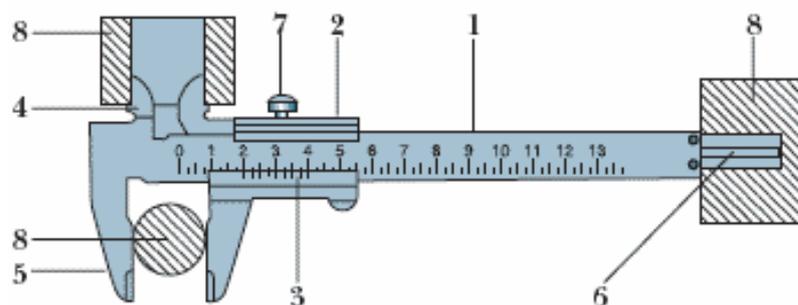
1 – штанга; 2 – ползун; 3 – нониус; 4 – верхние губки; 5 – нижние губки; 6 – глубиномер; 7 – стопорный винт; 8 – деталь, заготовка.
